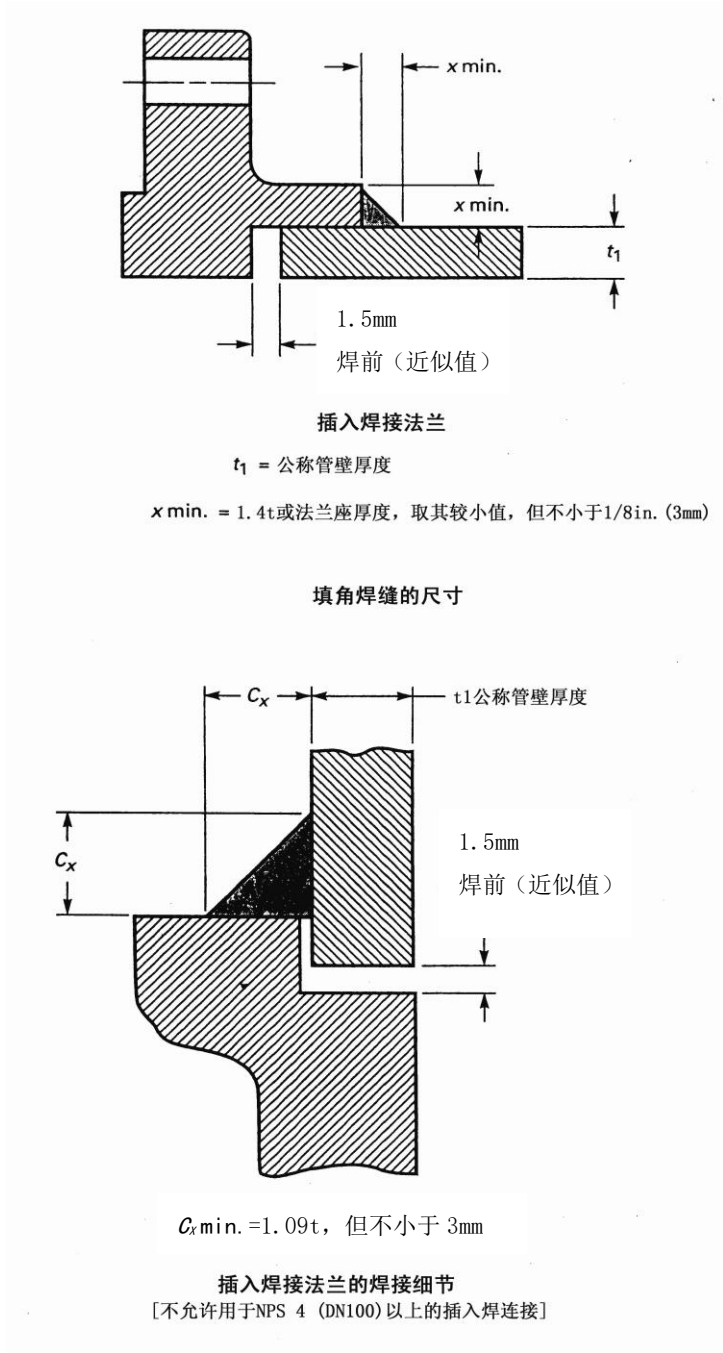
贴角焊缝和插入焊缝的尺寸 (续)
